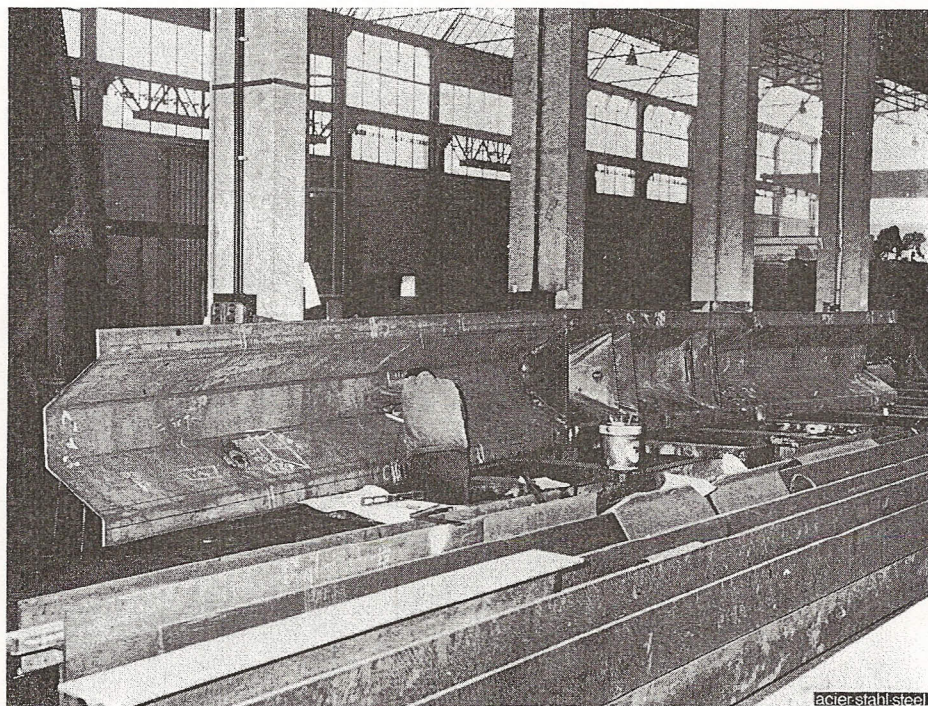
Fabbricazione di una delle piccole travi di sezione trapezoidale che servono all'ancoraggio dei cavi all'anello. Foto: Ferrini, Vicenza.
